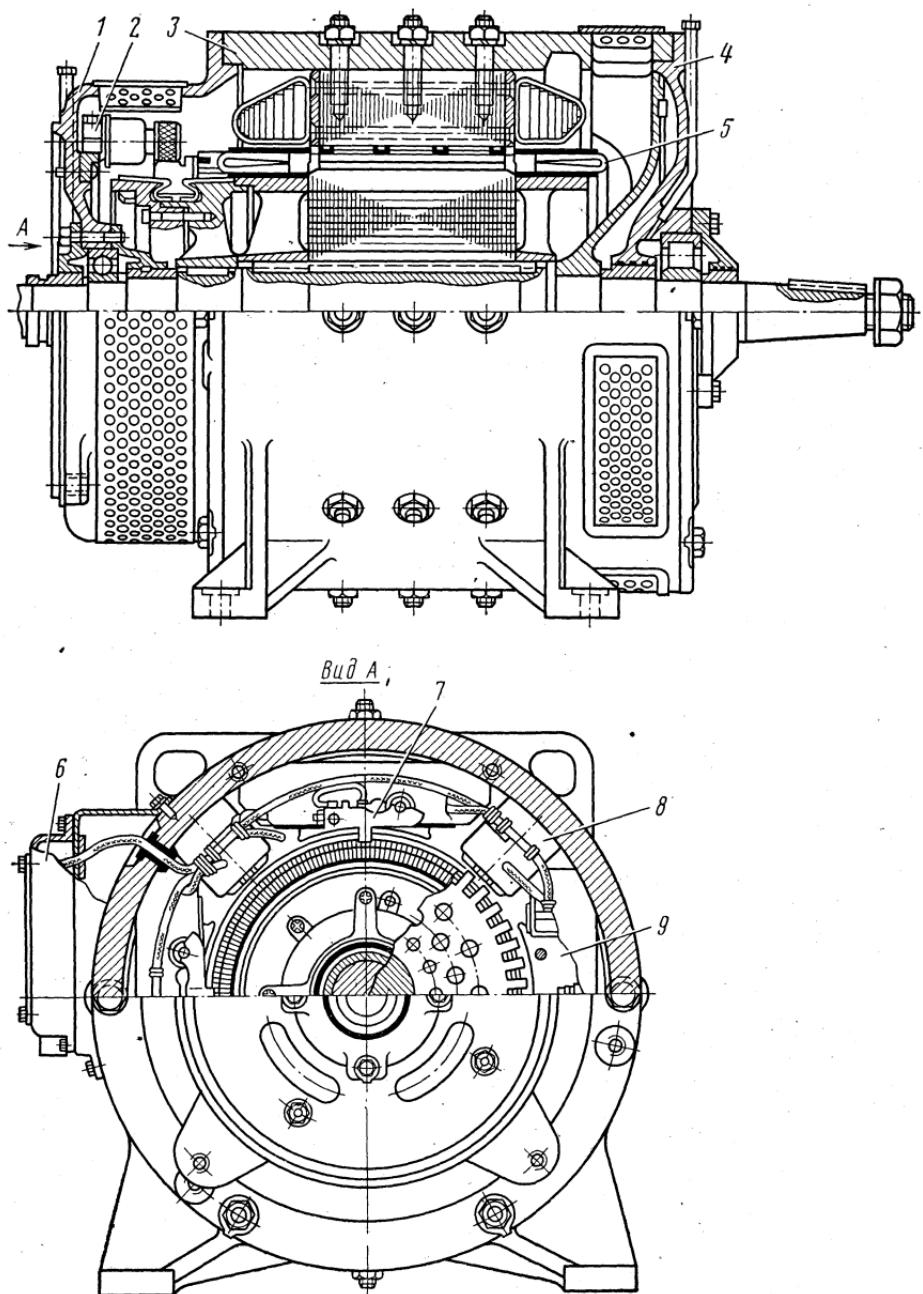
Продольный и поперечный разрезы электродвигателя НБ-430А:
